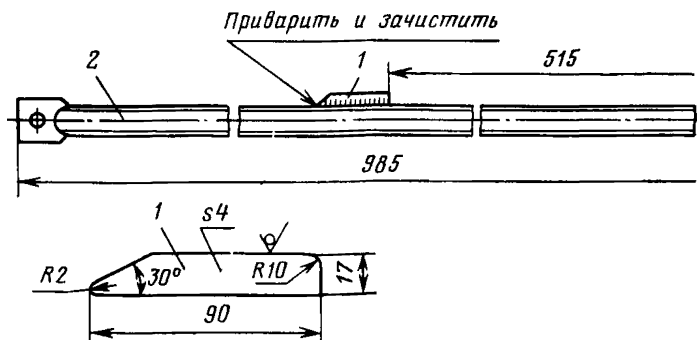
Тяга заземляющего разъединителя: 1 — косоугольная планка; 2 — тяга
